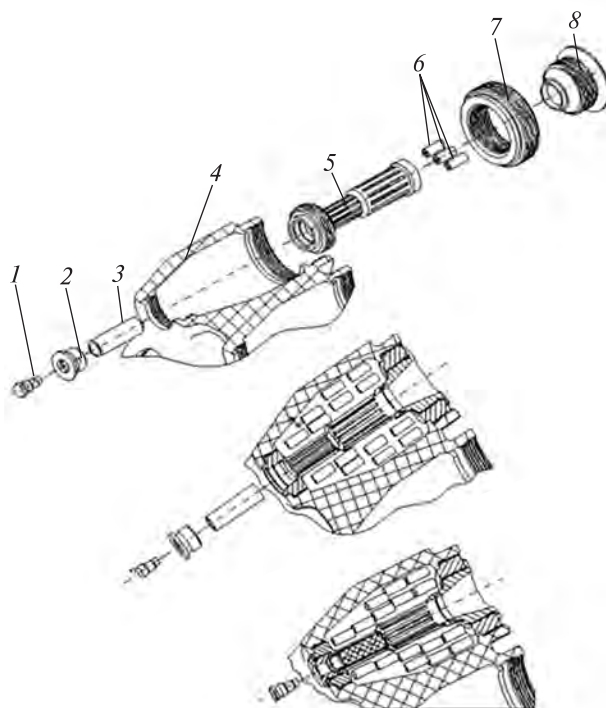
Схема сборки импульсных твердотопливных ракетных двигателей: 1 — пиропатрон, 2 — крышка, 3 — воспламенитель, 4 — корпус, 5 — трубка-диафрагма, 6 — заряд, 7 — гайка, 8 — сопло
